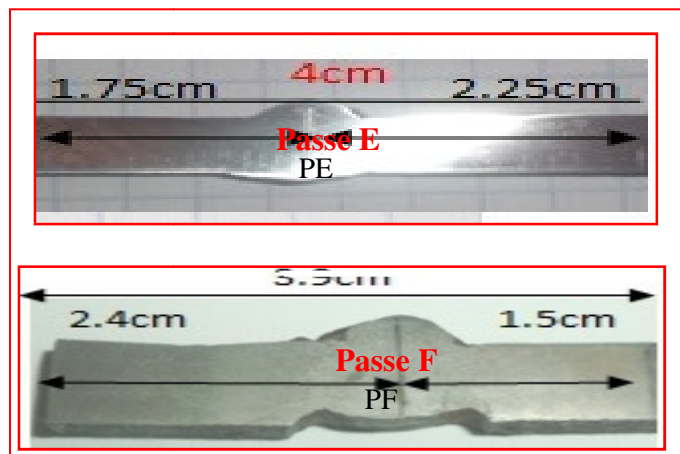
Macrographies en deuxième passe de soudage (PE et PF).
